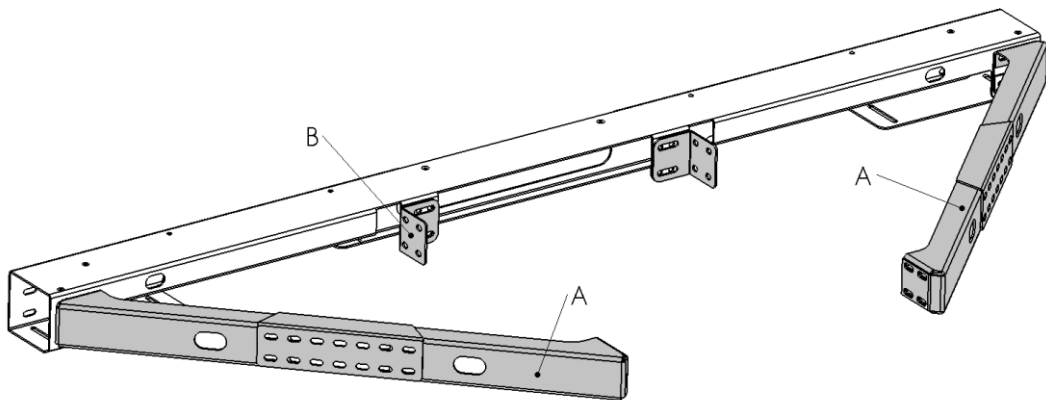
b Elementi di fissaggio della testata posteriore al controtelaio
